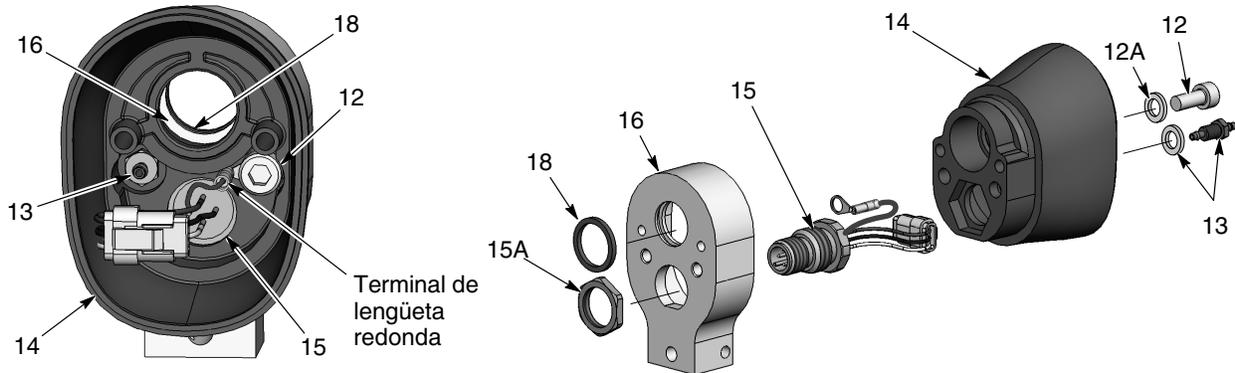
Desmontaje de la pistola de montaje en barra 3 de 3
